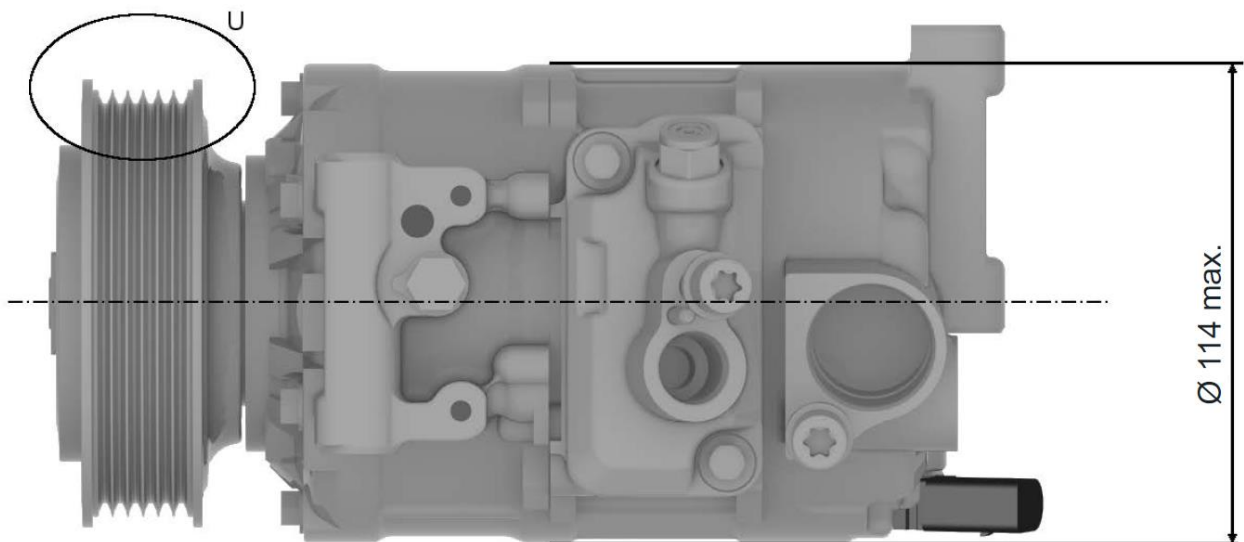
Размеры компрессора климатической установки Denso 6SU14 (вид сверху)
